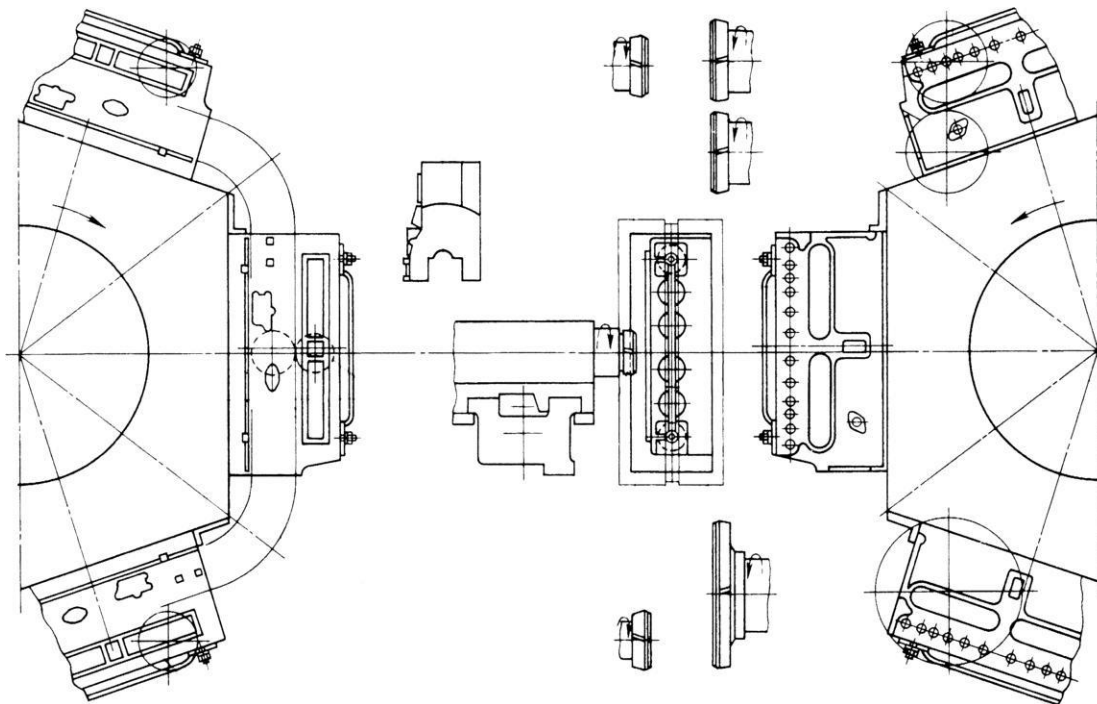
Схема фрезерування на карусельному барабанно-фрезерному верстаті
